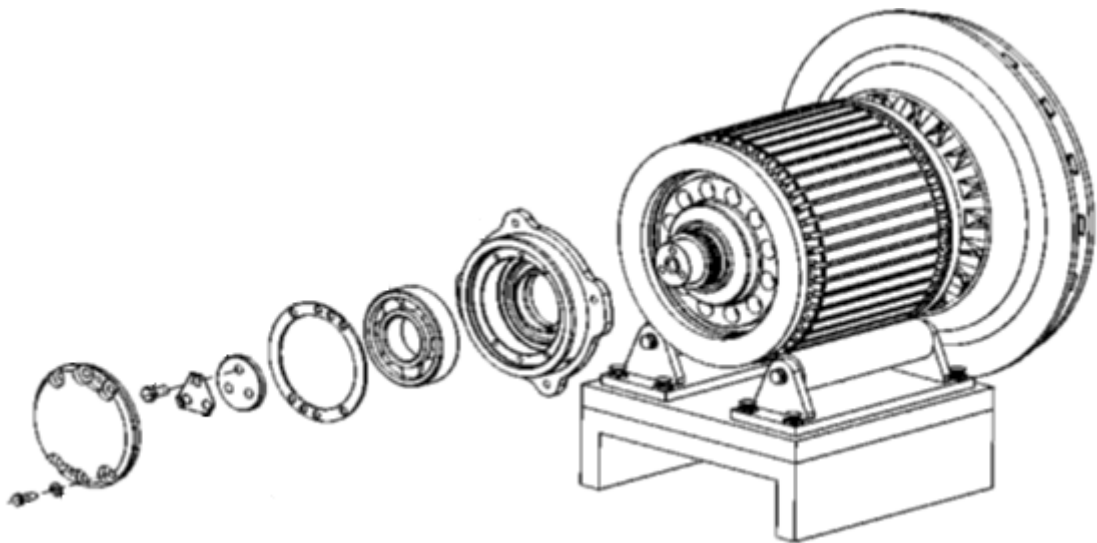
Rotor do Motor de Tração. Vista lado oposto ao acoplamento.
